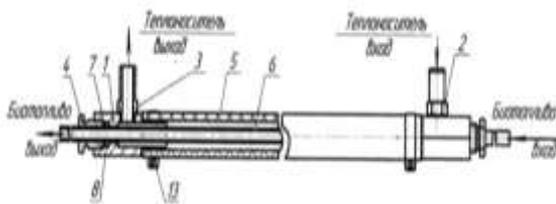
Подогреватель биотоплива: 1-корпус; 2-вход теплоносителя; 3-выход теплоносителя; 4-фиксирующая гайка; 5-резинотканевый рукав; 6-гибкий топливопровод; 7-уплотнительное кольцо; 13-крепёжный хомут.
